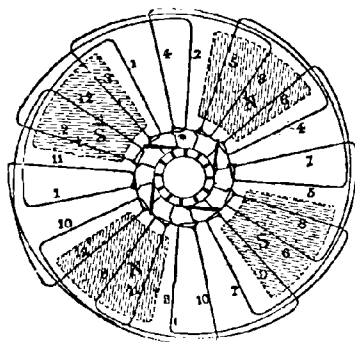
Bobinage imbriqué de disque à 4 pôles.
